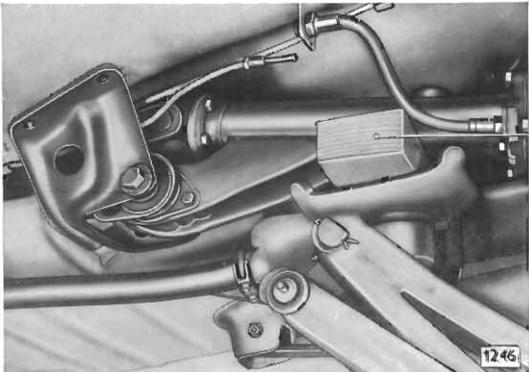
Hinterachse zum Befestigen der Gelenkbrücke
